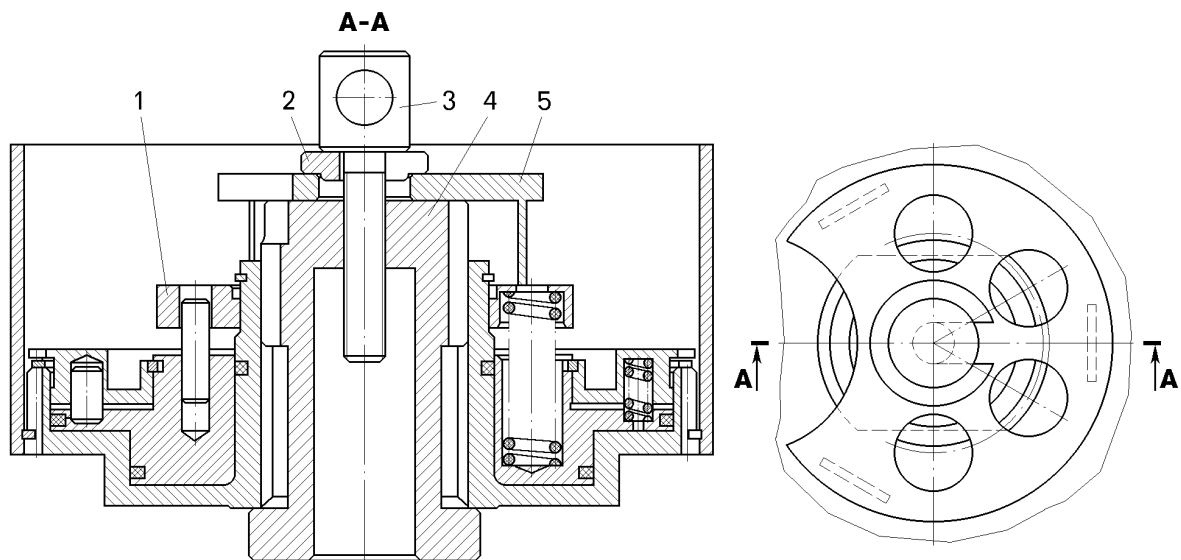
Приспособление для сборки и разборки фрикционов:
